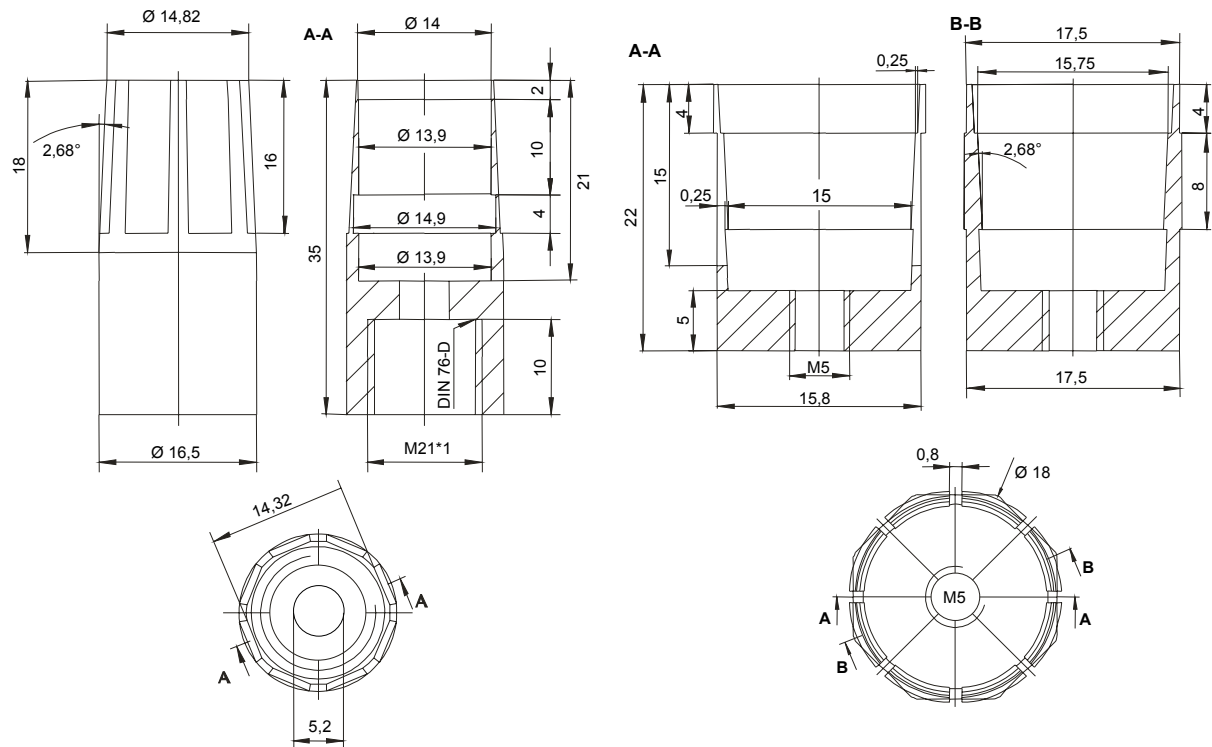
Zeichnung des innenverspannbaren eckigen Sensors des Typs AT9 / IT
